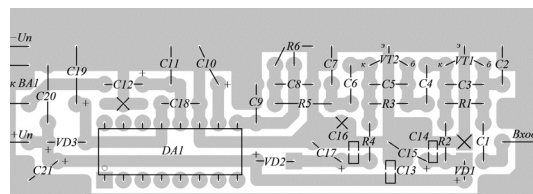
Эскиз платы УЗЧ – 1. Вид со стороны установки деталей. Крестами обозначены проволочные перемычки между фольгой общего провода с обеих сторон платы. Конденсаторы C13, C14 и C16 – SMD, типоразмер – 0805...1206 устанавливаются со стороны печатных проводников. Общий провод входа УЗЧ припаивается вблизи от эмиттера VT1, плата соединяется с входным гнездом скрученной парой (общий и фазный провода), при сильных наводках, одновременно двумя проводами наматываются обмотки до заполнения на ферритовом кольце, которое помещается у самой монтажной платы
